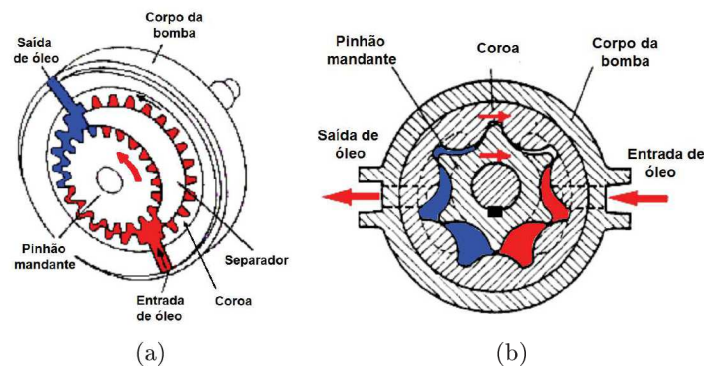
Bomba de engrenagens de dentado interno direito; b) Bomba de engrenagens de dentado interno do tipo rotor. Adaptado de [16].
